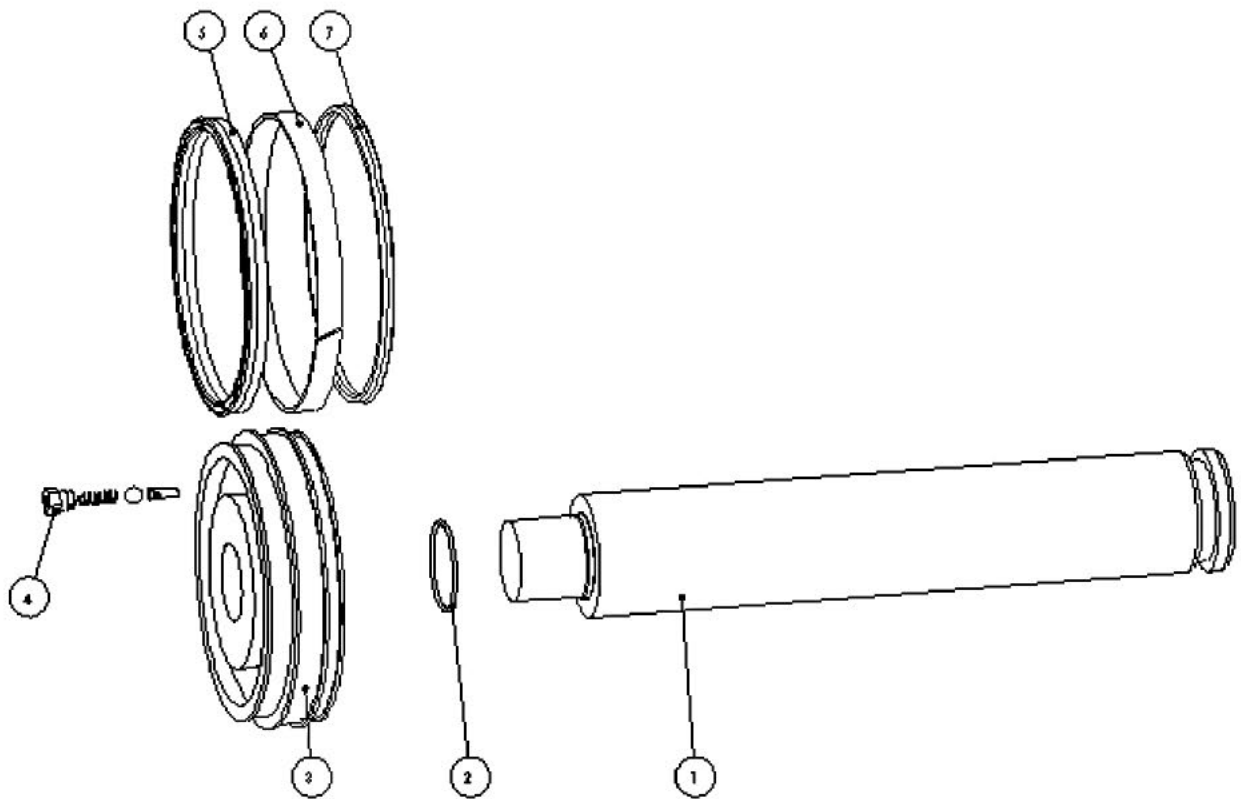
Rozpadové schéma 2 - Hydraulický systém
